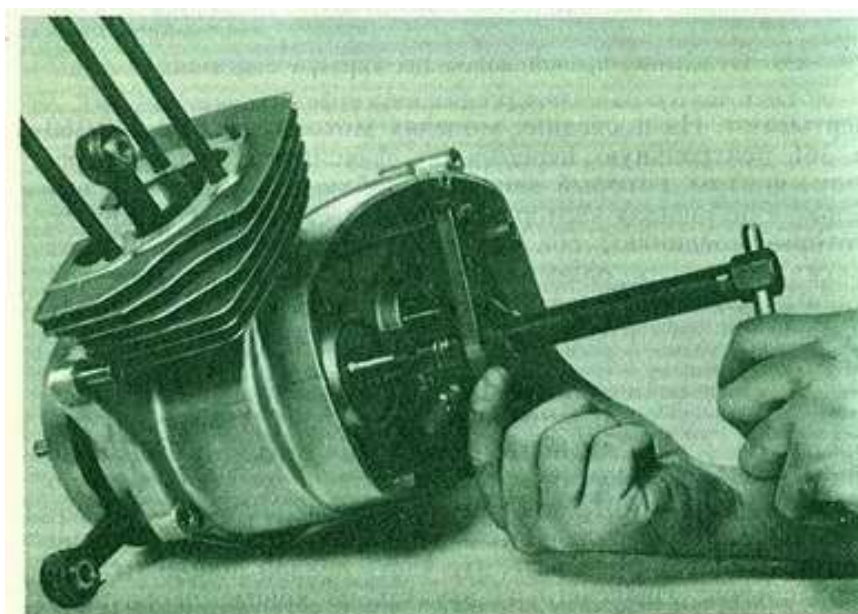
Выпрессовка кривошипно-шатунного механизма из картера
